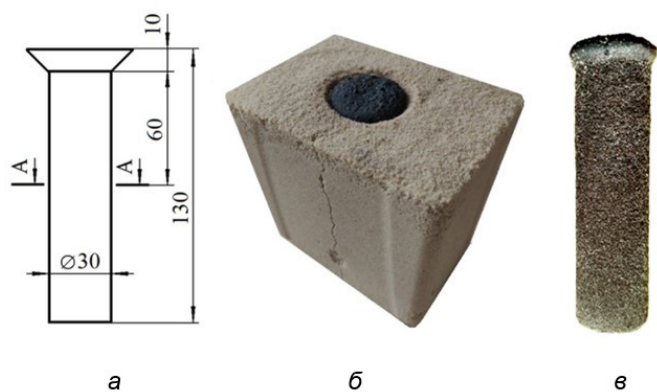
Схема циліндричного зразка (а), вид залитої ливарної форми (б) і вибитого з форми зразка (в)
